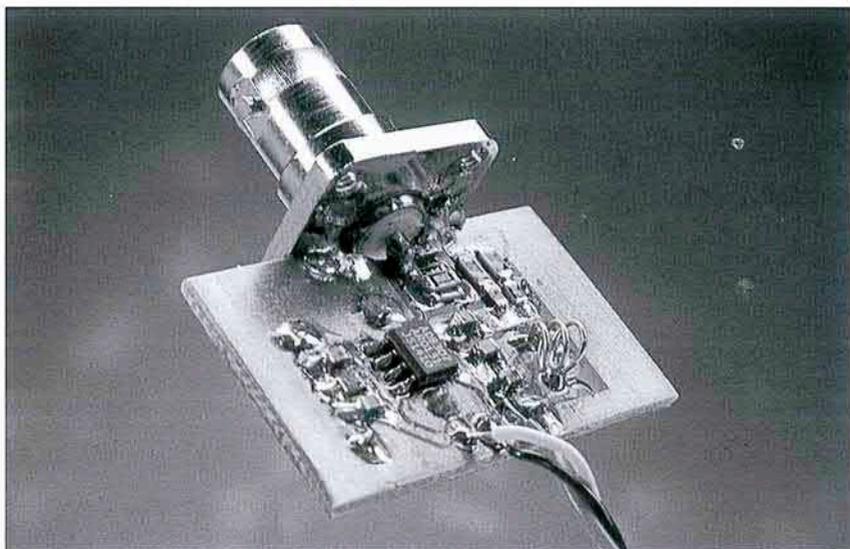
La placa de entrada con el conector BNC conectado a la misma directamente y soldado a lo largo de todo el borde.
